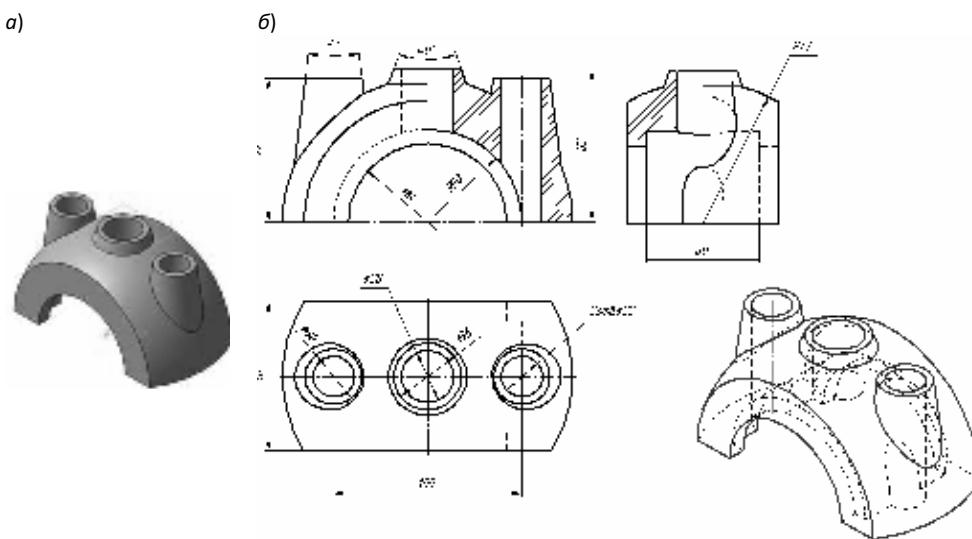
Компьютерная модель и ассоциативный чертеж корпусной детали
